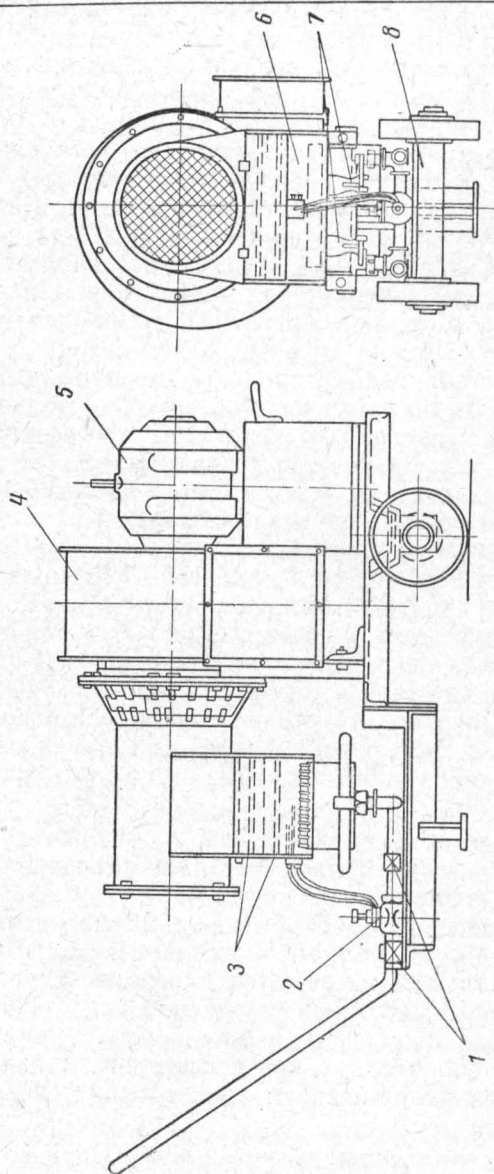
Схема газовой сушильной установки конвективного типа КС-АКХ
